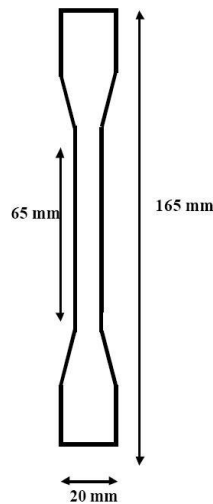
Géométrie des éprouvettes lisses.
